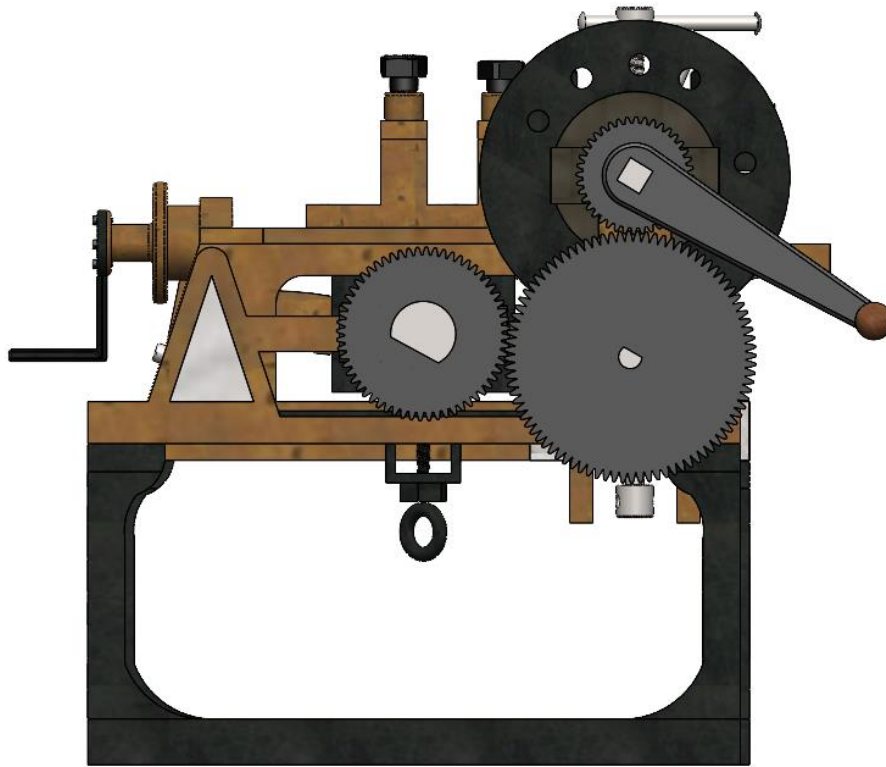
Sistema de transmisión de movimiento mediante engranajes.
